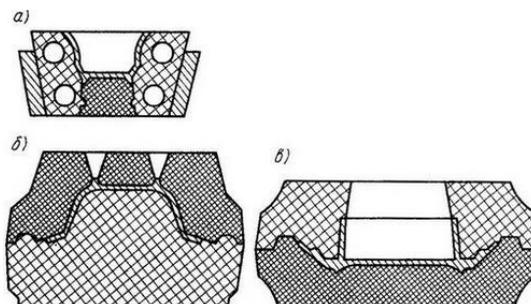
Способы отливки в гипсовых формах: а – наливной; б – сливной; в – комбинированный
